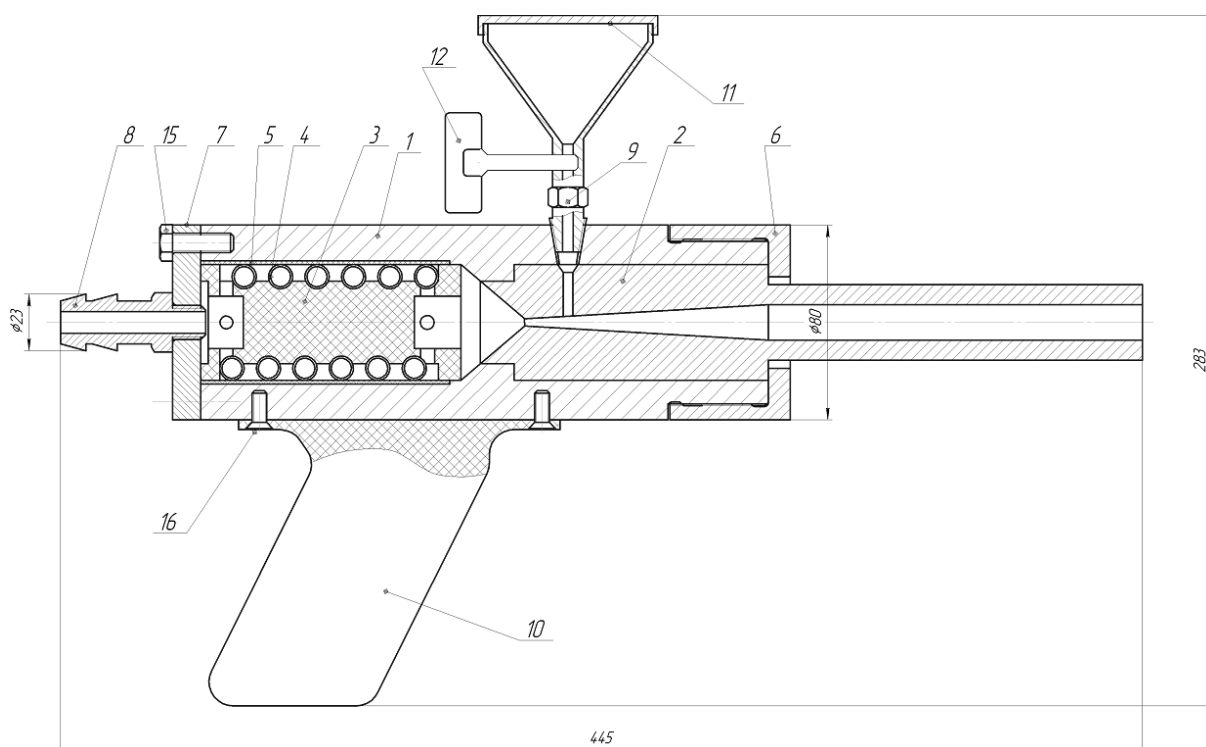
Газодинамічний напилювальний пристрій:
